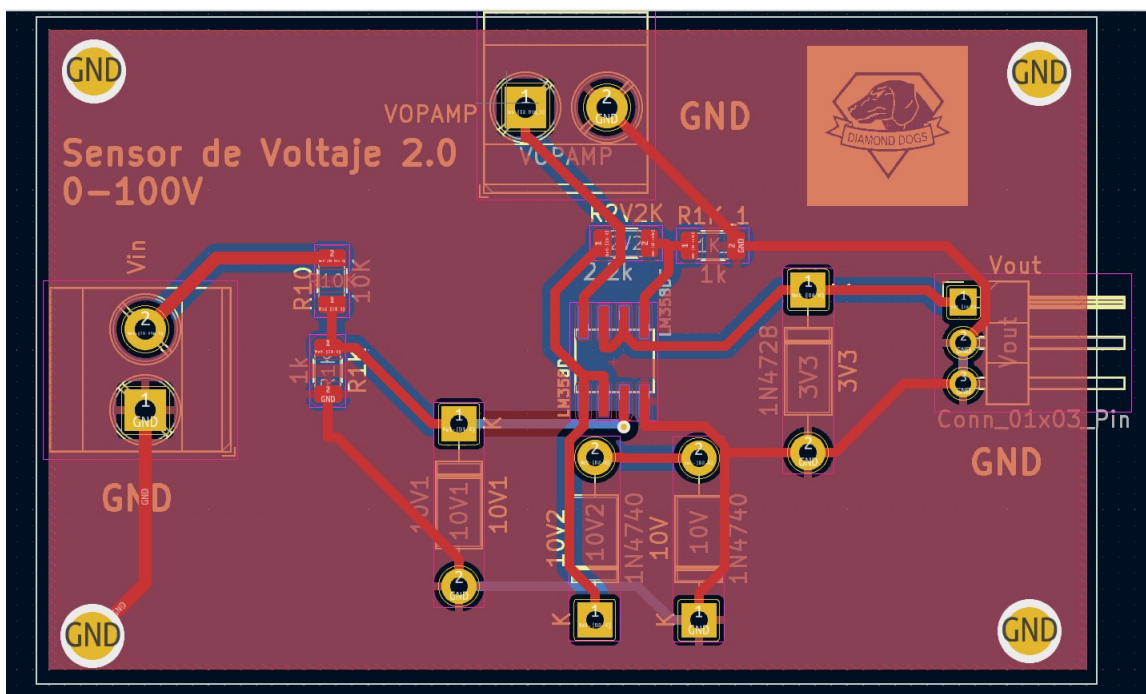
PCB Voltage Sensor, Input 0-100V, Output 0-3.3V
